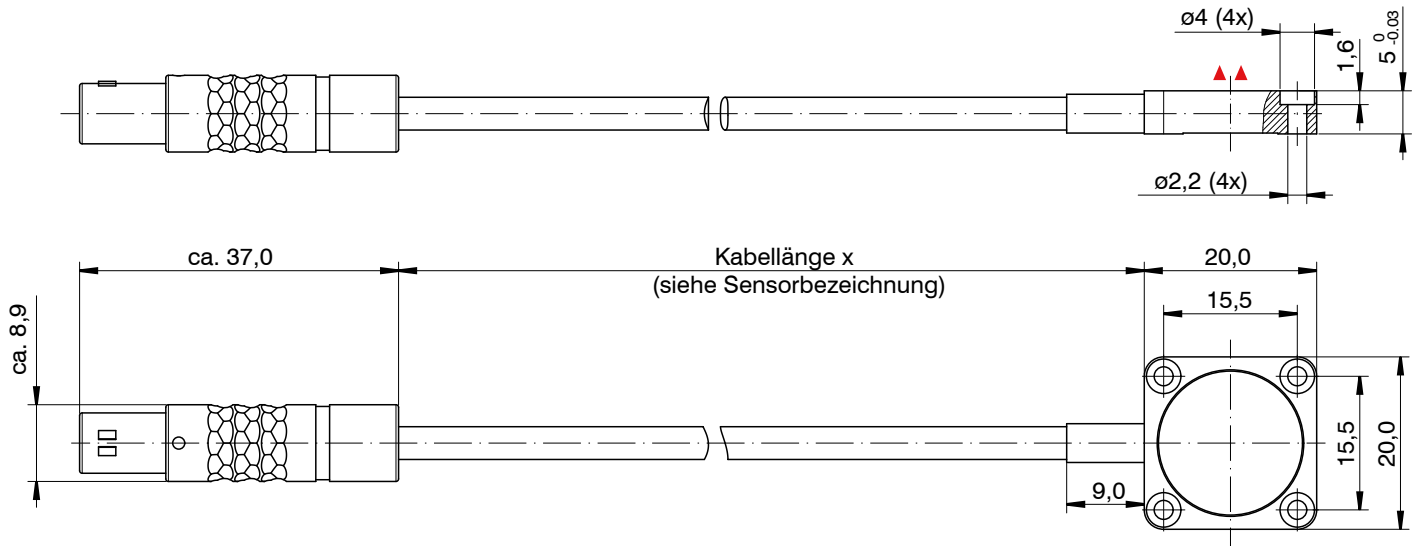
Maßzeichnung Flachsensor CSHA2FL-CRAxx mit integriertem Kabel, Messbereich 2 mm nominal, Abmessungen in mm
